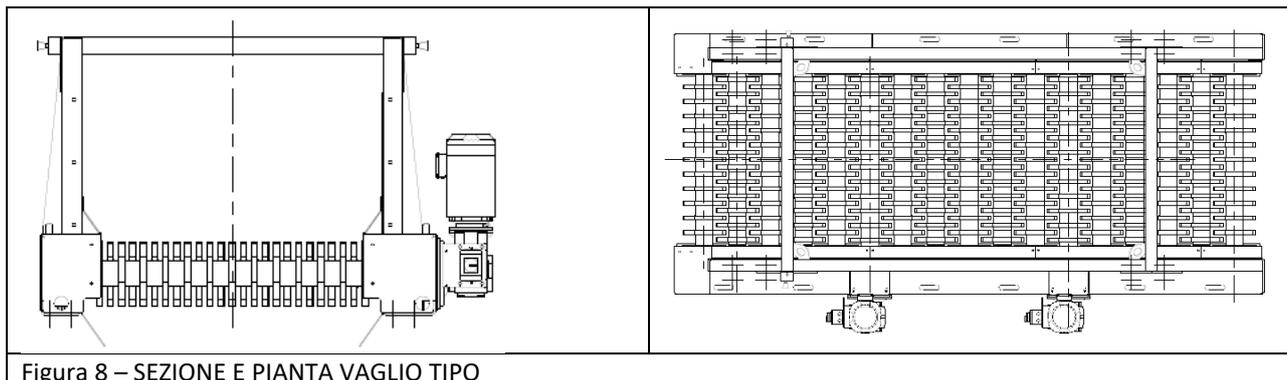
SEZIONE E PIANTA VAGLIO TIPO
